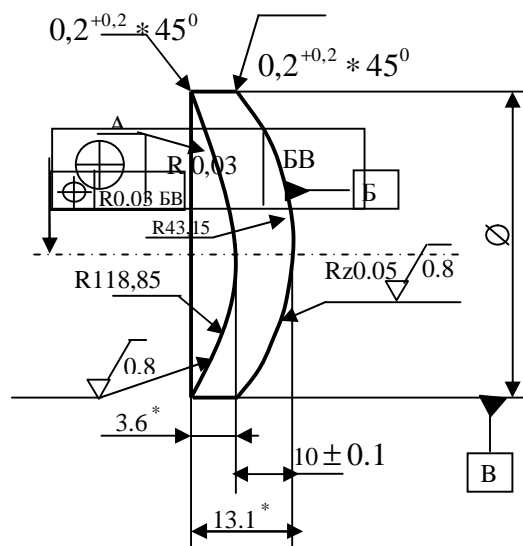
Эскиз линзы с допусками на центровку
